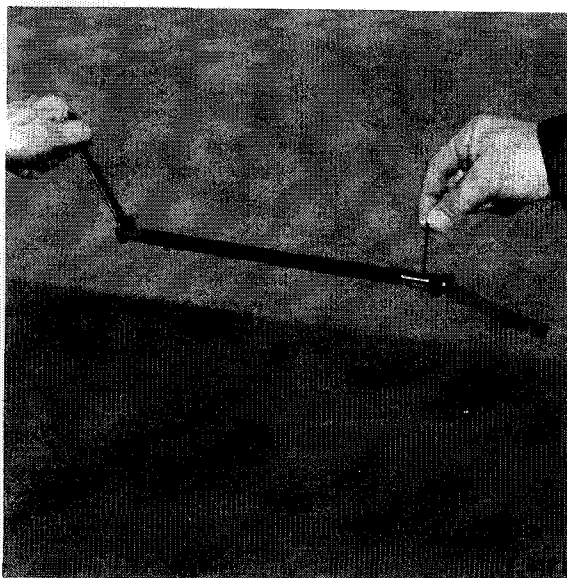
Vorrichtung zum Einstellen der Regelzahnstange
